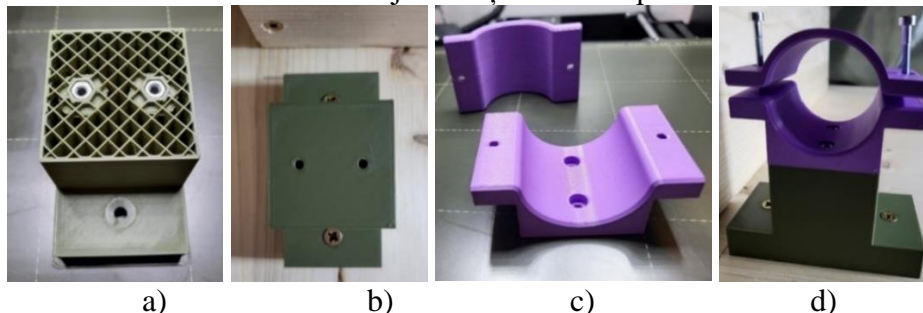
Suport motor V2: a) Piulițe imprimate în piesa fixă; b) Montare piesă fixă; c) Parte mobilă; d) Ansamblul sistemului de prindere-fixare a motorului standului.
